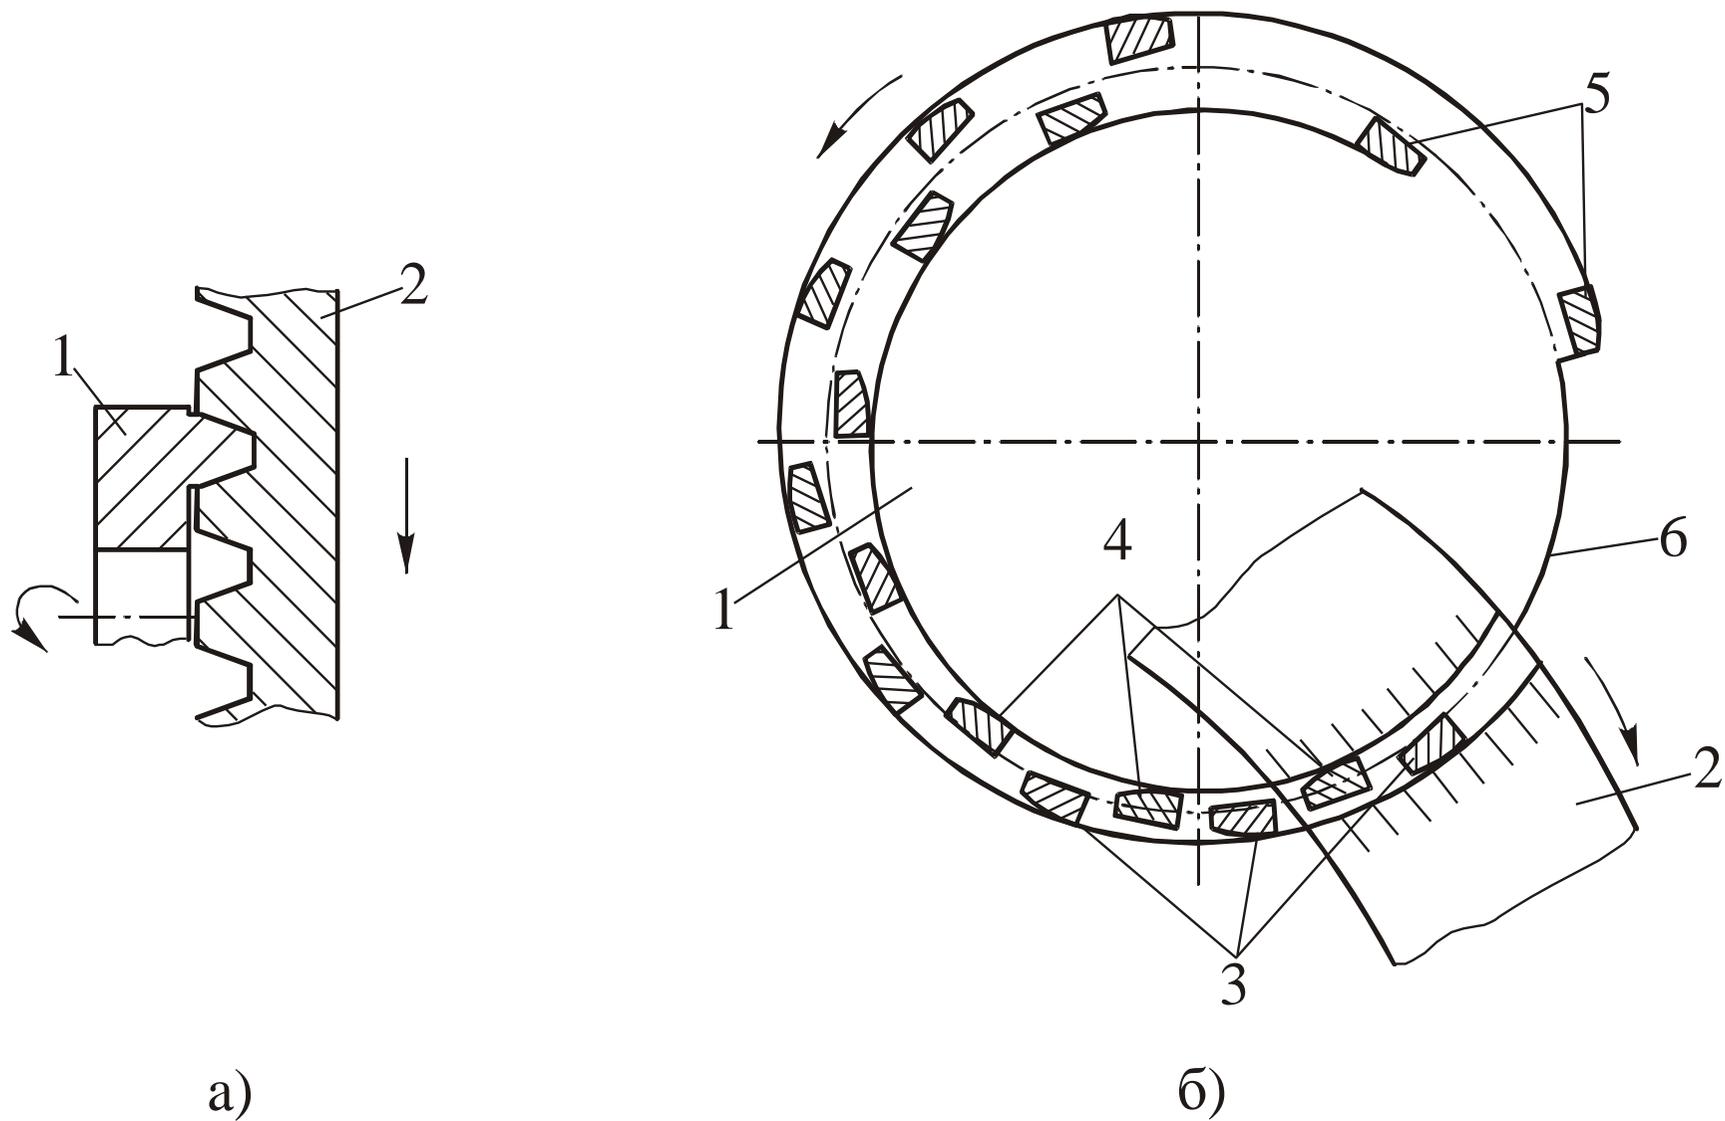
Нарезание головкой-протяжкой криволинейных зубьев конических колес: *а* – схема резания; *б* – головка-протяжка
